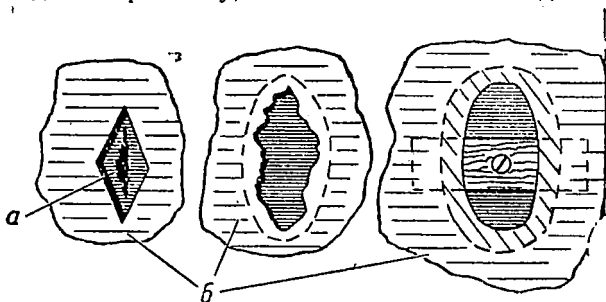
Способы ремонта незначительных повреждений фанерной обшивки; а—трещина; б—фанерная обшивка.
